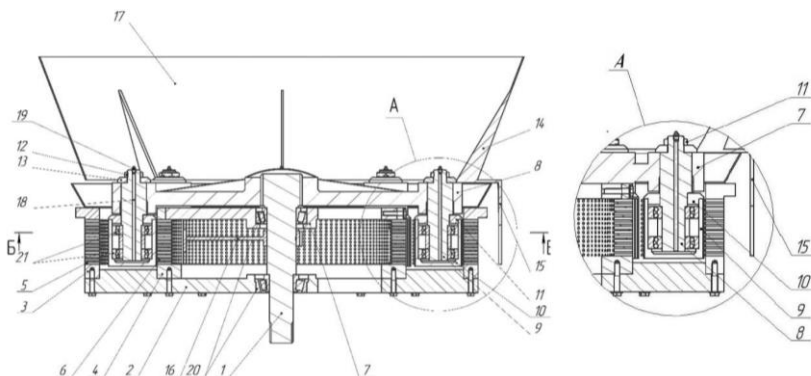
Общий вид двухматричного пресс-гранулятор:
